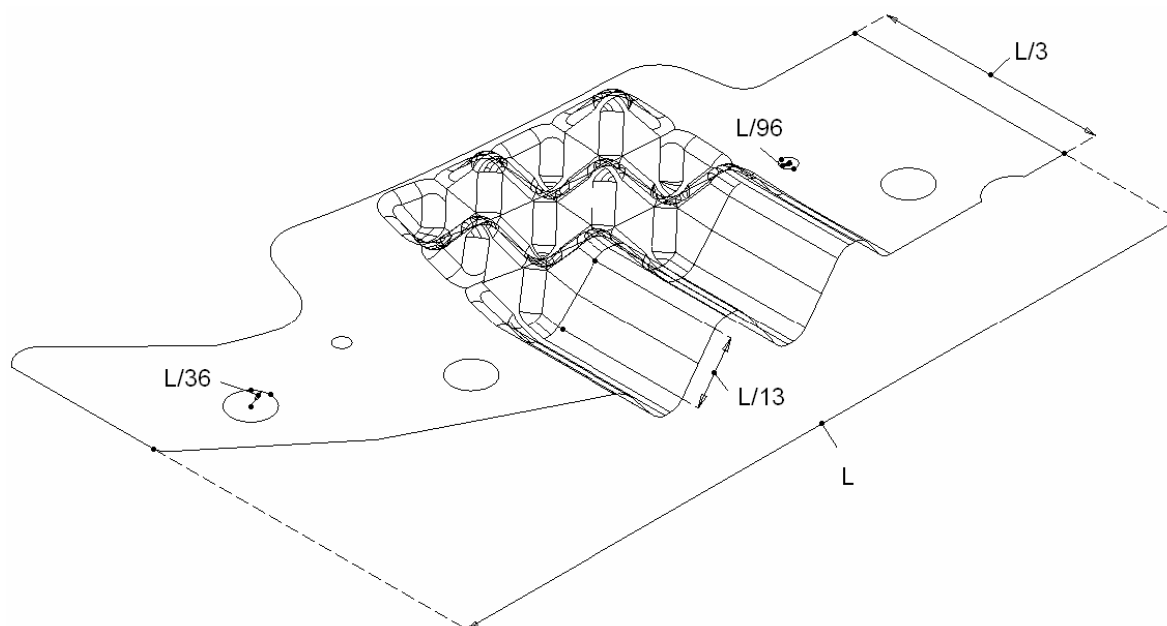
Forme de la pièce et données dimensionnelles en vue isométrique.
